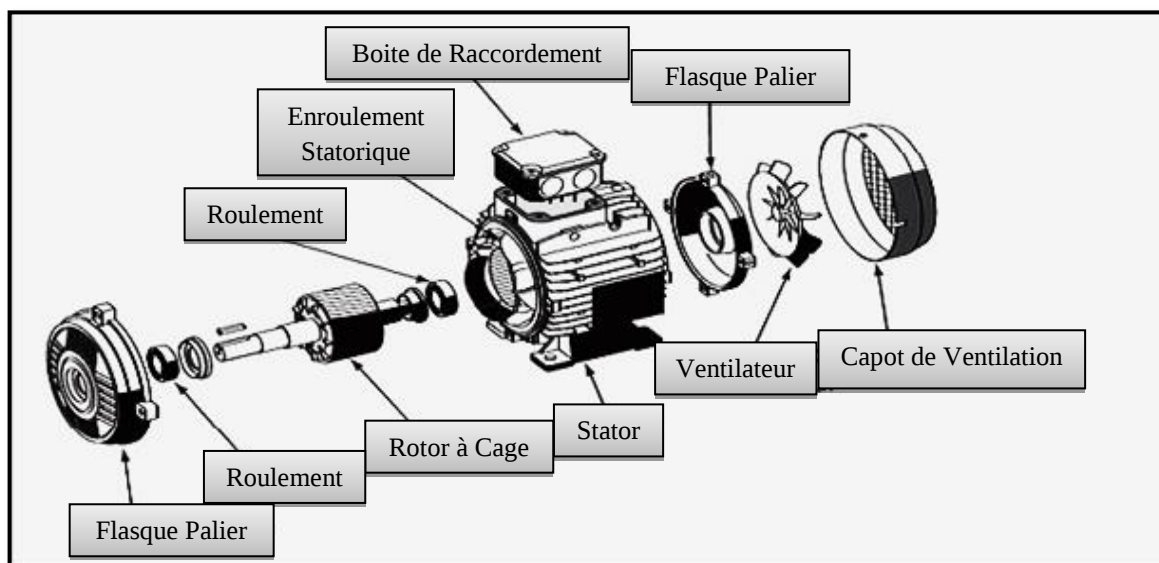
Vue éclatée d'un moteur asynchrone [1]
